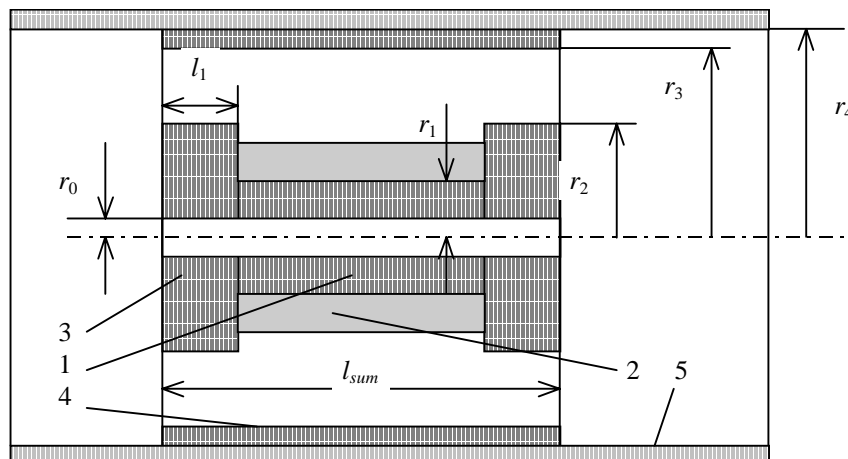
Схема конструкции индуктора магнитной установки УМП:
